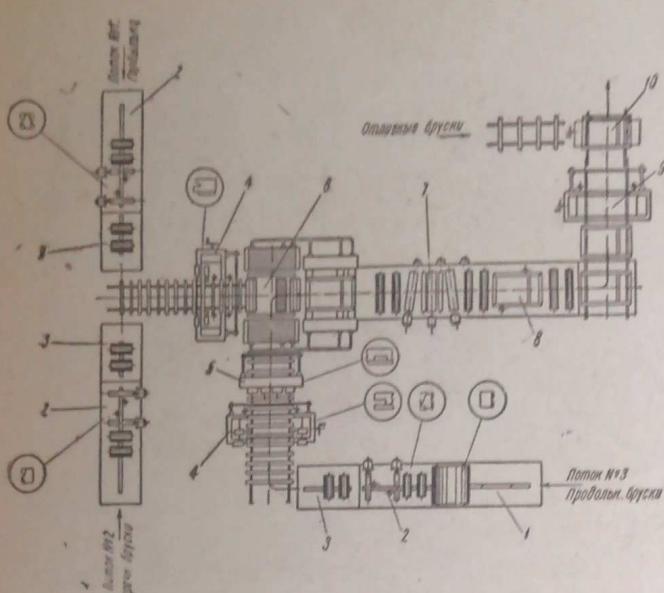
Деревообделочный комбайн с единой кинематической схемой без промежуточного распределителя
